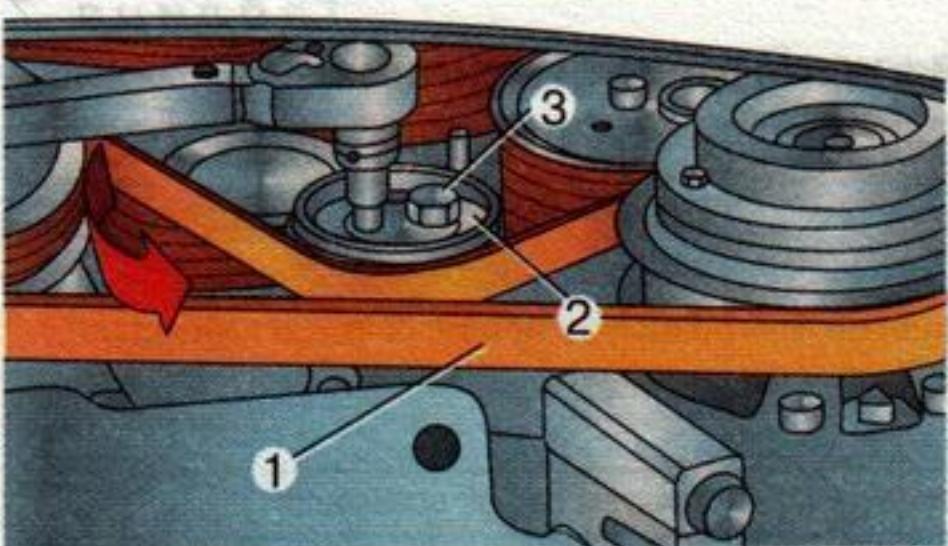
Снятие и установка ремня привода компрессора кондиционера дизельного двигателя рабочим объемом 2,5 л: 1 – ремень привода компрессора кондиционера; 2 – натяжной ролик; 3 – стопорный болт
